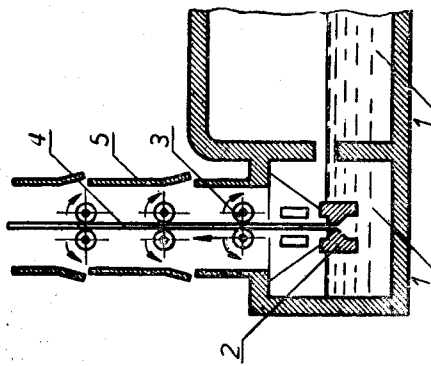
Procedeul Fourcault de fabricare a geamurilor : 1 — zona de lucru a cuptorului ; 2 — duza din material refractar ; 3 — valțuri ; 4 — bandă de geam ; 5 — cheson.
